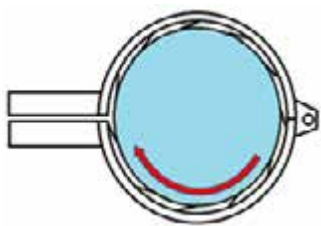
Направление вращения шейки вала при полировке охватывающими щипцами должно помогать формировать микроворсинки применяемым абразивным материалом; источник: TB2052 DANA
